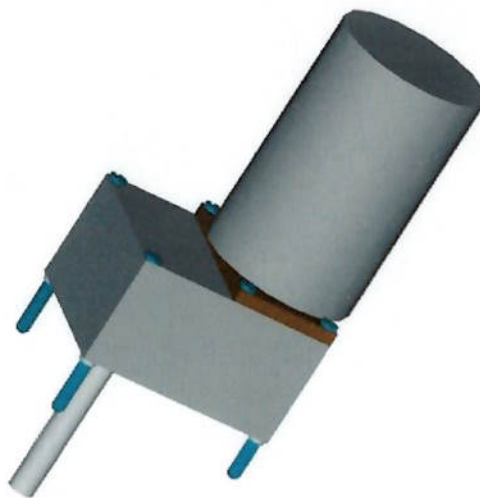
Motor seleccionado para as rodas: P4742 (203-13575), fabric. AJMaia.
